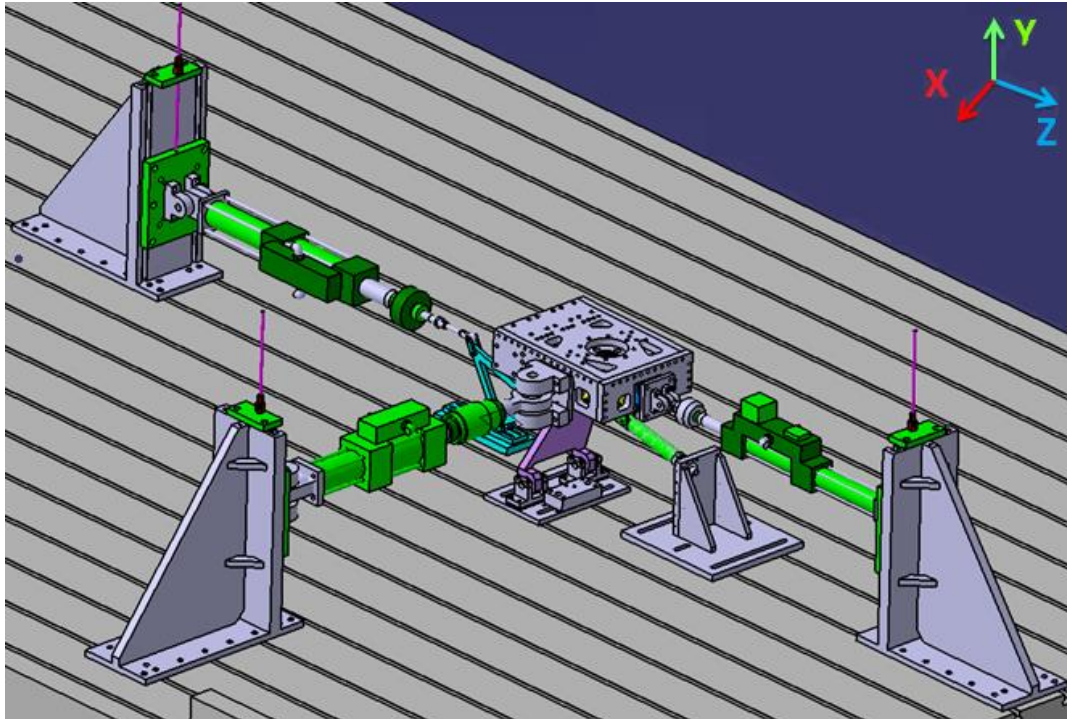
Layout de la disposición Longitudinal en Catia. Vista 1
